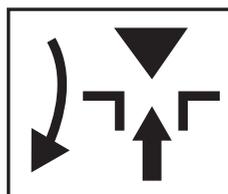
Табличка, указывающая направление вращения регулировочного болта
